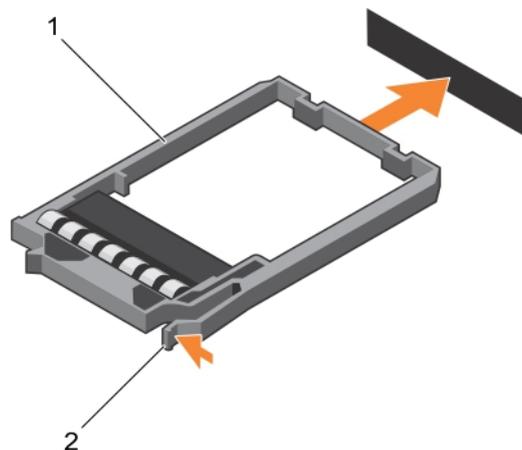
Installieren eines 1,8-Zoll-SSD-Platzhalters
